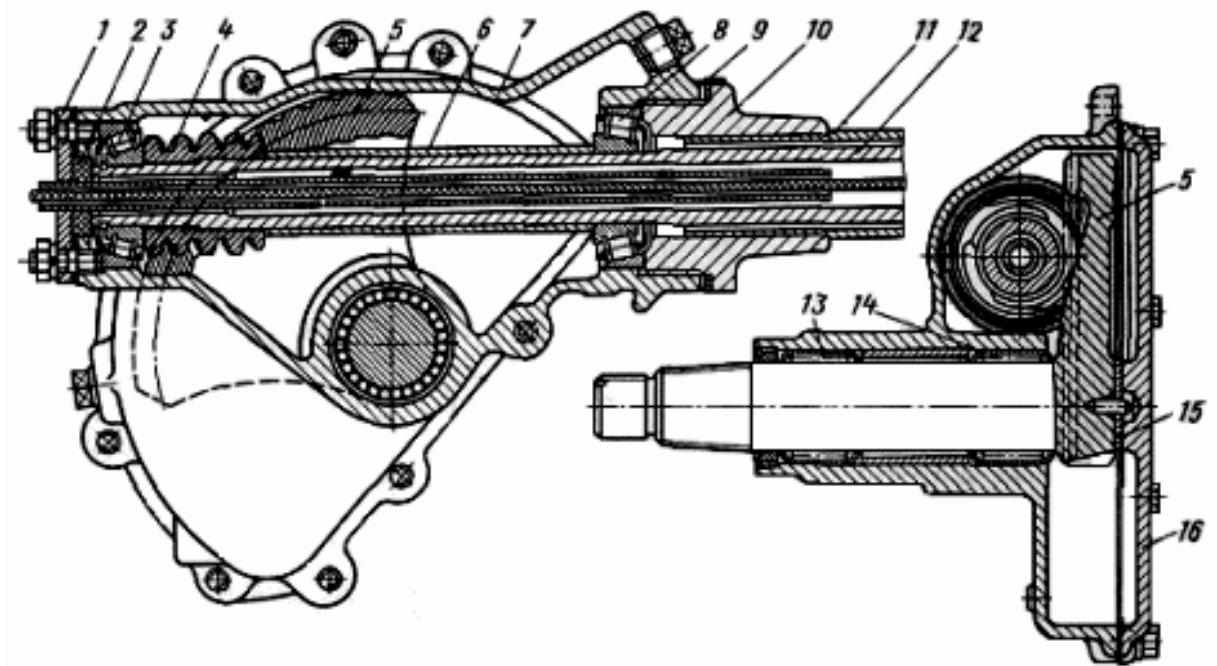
Рулевой механизм автомобиля КраЗ-156: 1 - нижняя крышка; 2 - сальник; 3 и 8 - конические роликовые подшипники; 4 - червяк; 5 - сектор; 6 - распорная втулка; 7 - катер; 9 - регулировочные прокладки; 10 - верхняя крышка; 11 - колонка; 12 - вал рулевого механизма; 13 и 14 - игольчатые подшипники; 15 - упорная шайба; 16 - боковая крышка
